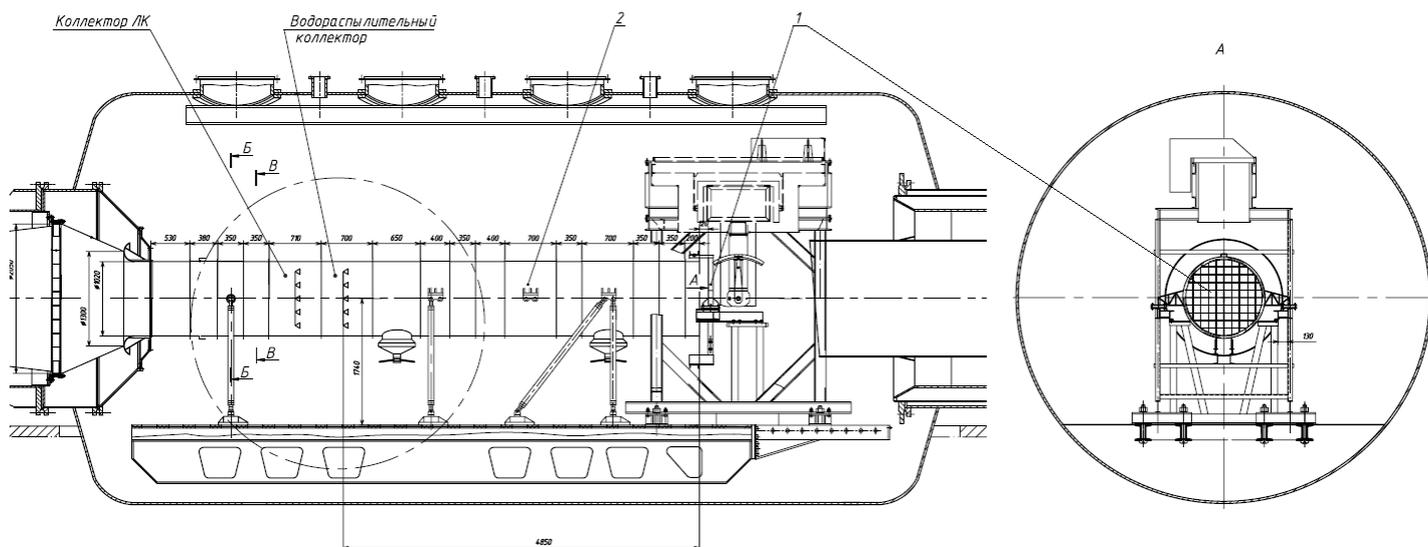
Общий вид установки для проведения калибровочных испытаний потока с ЛК: 1 – мерная решётка, 2 – АДТ
